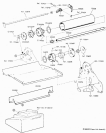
SPALMONTAGGIO E MONTAGGIO DELLA VERSIONE
